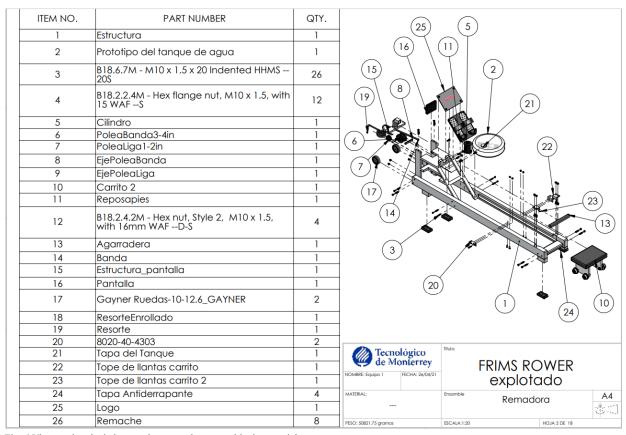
Vista explotada de la remadora completa con tabla de materiales.
